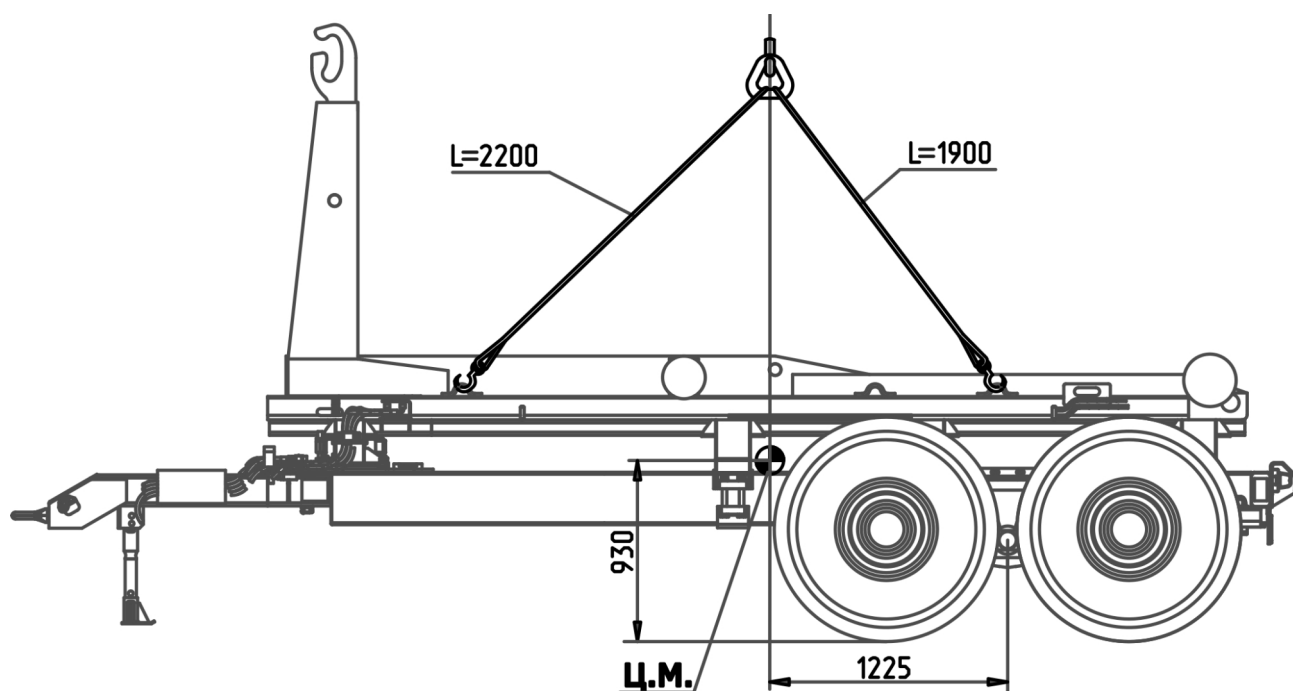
Схема строповки полуприцепа без контейнера
